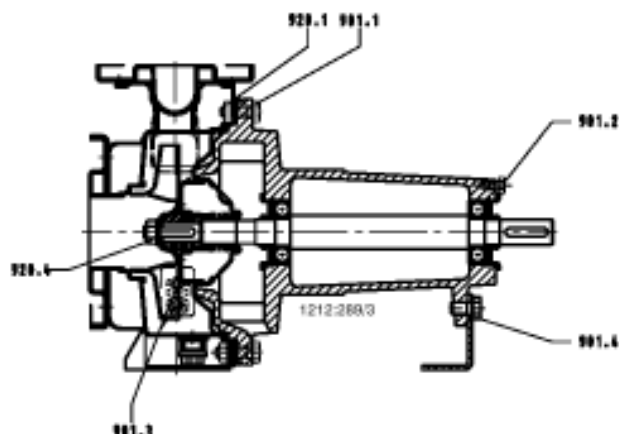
Места затяжки резьбовых соединений Etachrom NC с диаметром рабочего колеса 125, 160, 200, исключая 50-200, 65-200, 80-200
